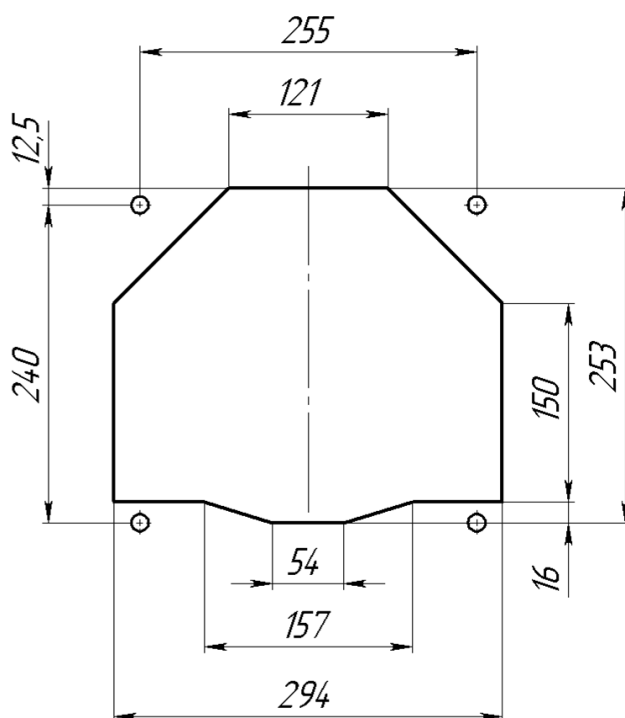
Габаритные размеры монтажного отверстия в дверце котла
